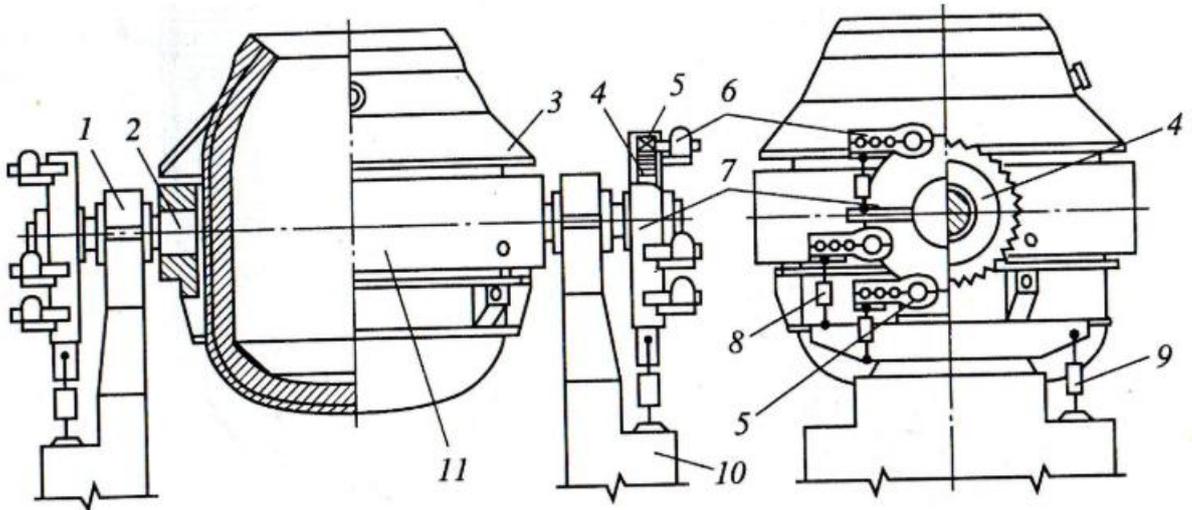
Кислородный конвертор с двухсторонним навесным многодвигательным механизмом поворота: 1 – опорный подшипник, 2 – цапфа, 3 – защитный кожух, 4 – ведомое зубчатое колесо, 5 – вал-шестерня, 6 – навесной электродвигатель с редуктором, 7 – корпус ведомого колеса, 8,9 – демпфер, 10 – опорная станина, 11 – опорное кольцо.
